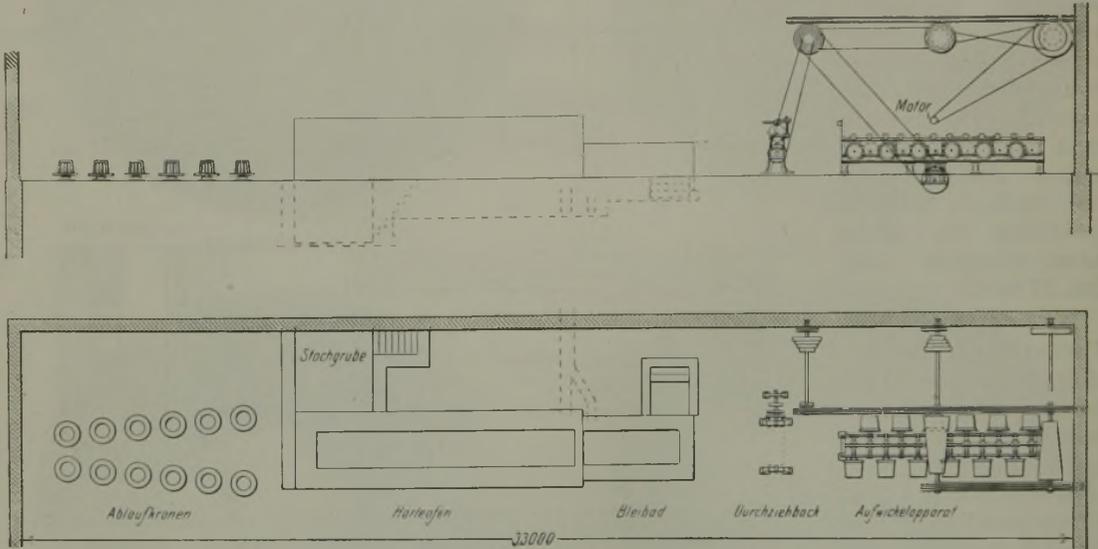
Lageplan einer Drahtvergütungsanlage von Möhl & Co., Dellbrück.
